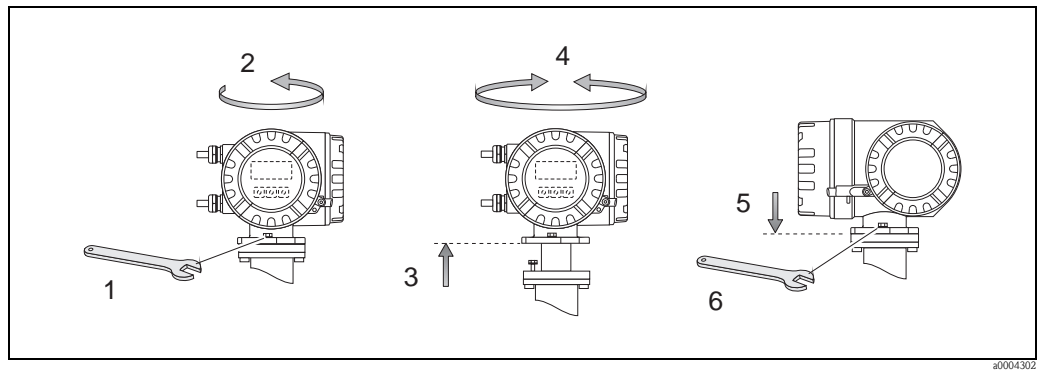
Drehen des Messumformergehäuses (Aluminium-Feldgehäuse)
